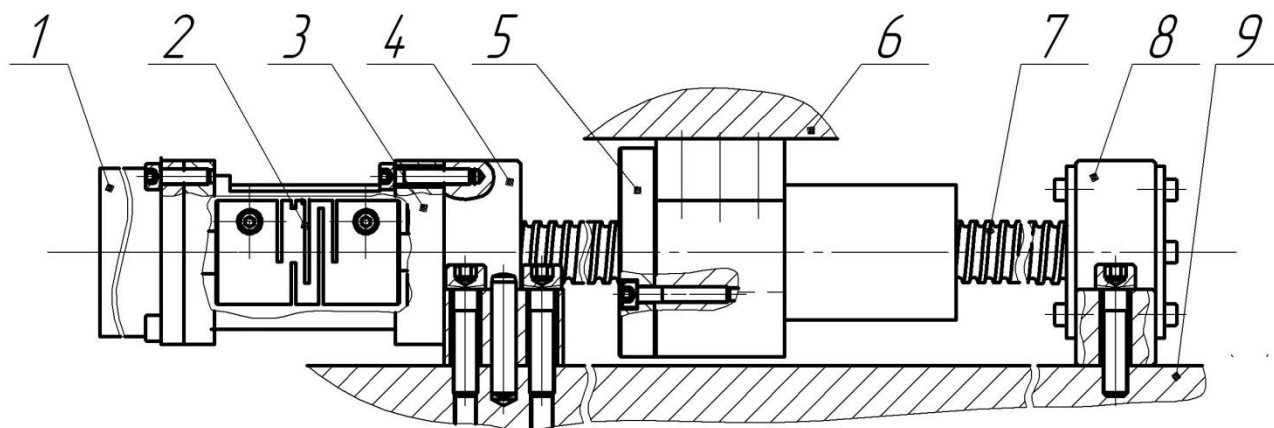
Конструктивная схема привода поперечной подачи: 1-серводвигатель; 2-муфта; 3-стакан; 4-передняя опора; 5-гайка ШВП; 6-поперечные салазки; 7-ходовой винт ШВП; 8-задняя опора; 9-продольные салазки
